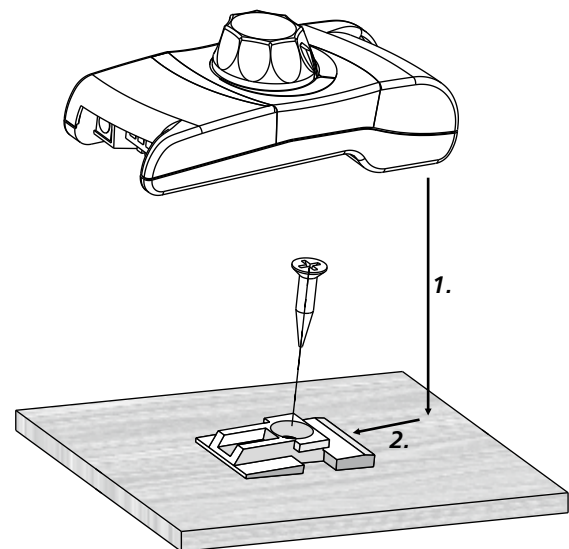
Das Befestigen des Gerätes auf einer Grundplatte
